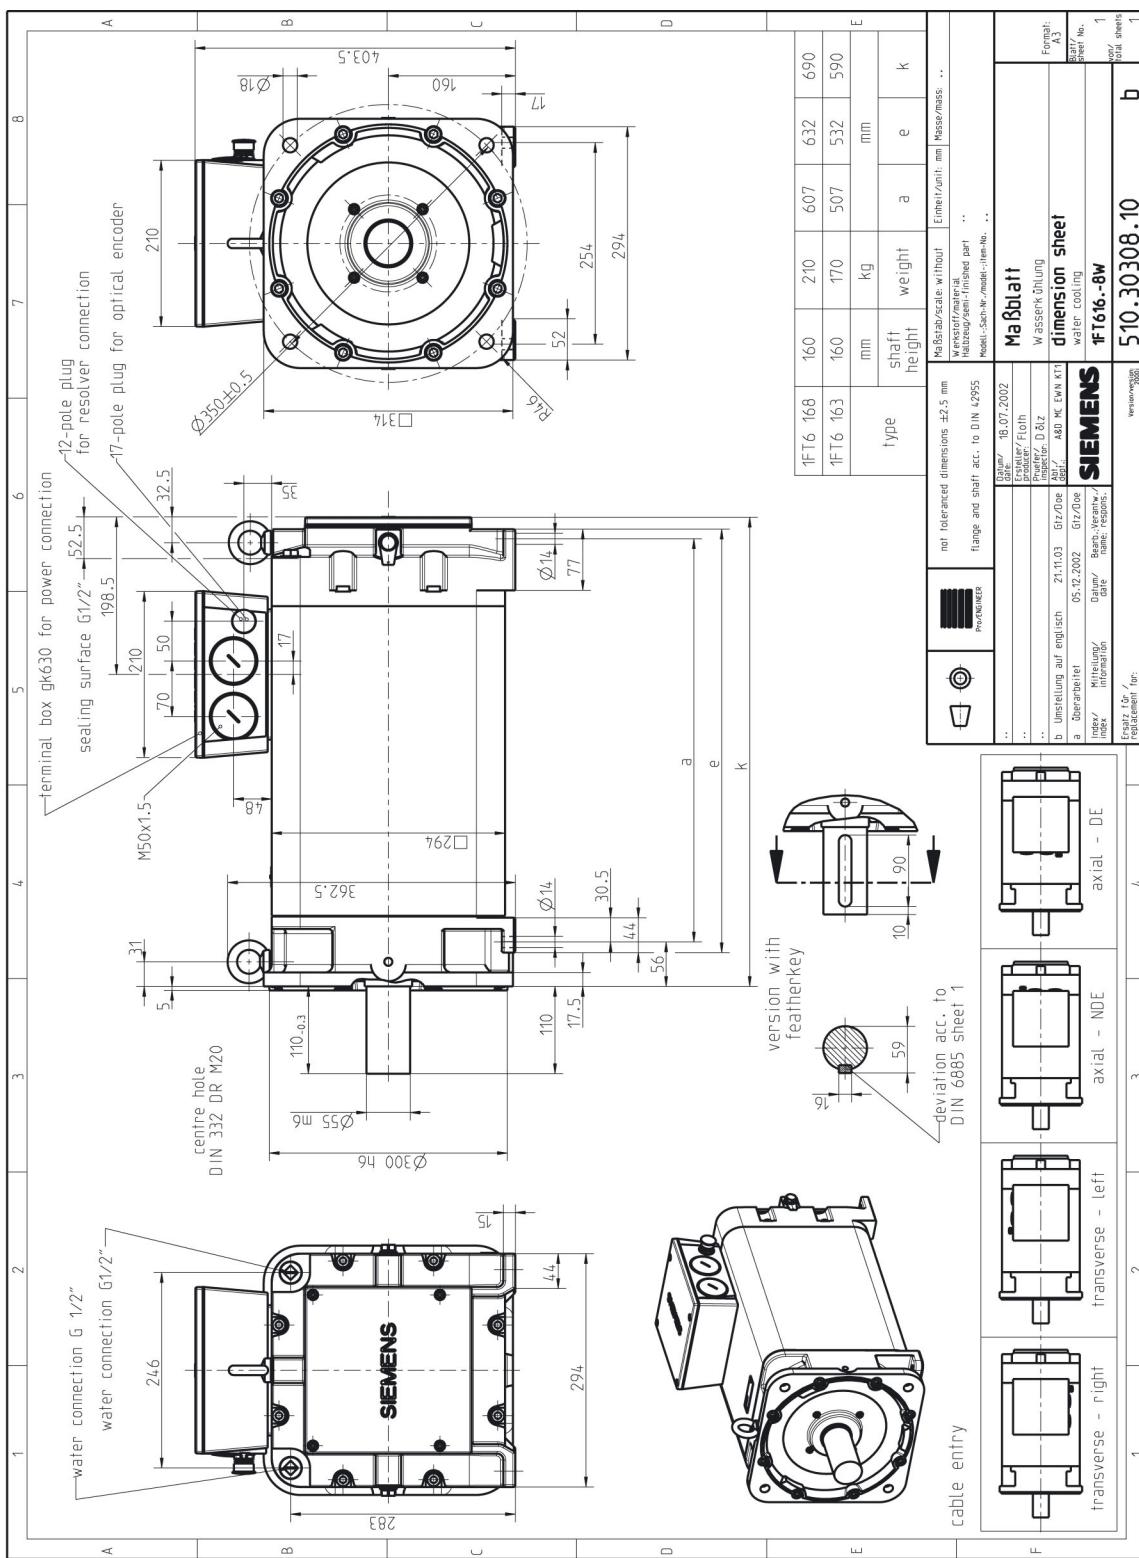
1FT616□ wassergekühlt mit Klemmenkasten
